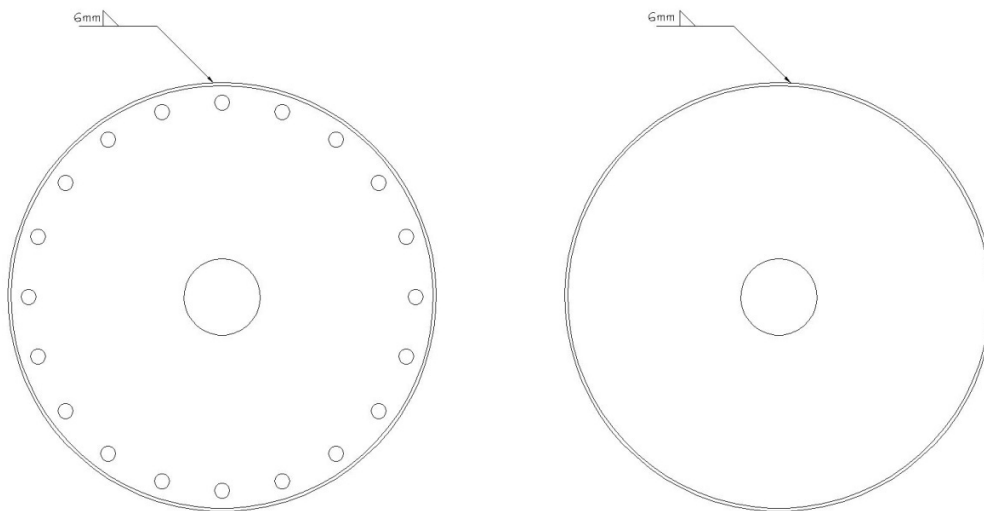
Detalle de soldadura para tapas del cilindro.
